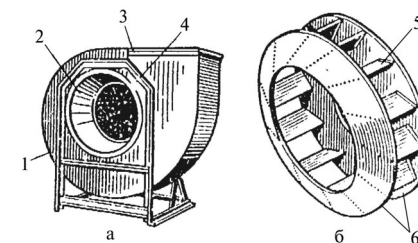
Відцентровий вентилятор: а - загальний вигляд; б - робоче колесо; 1 - корпус (кожух); 2 - вхідний патрубок; 3 - вихідний патрубок; 4 - станина; 5 - робоча лопать; 6 - диски.
